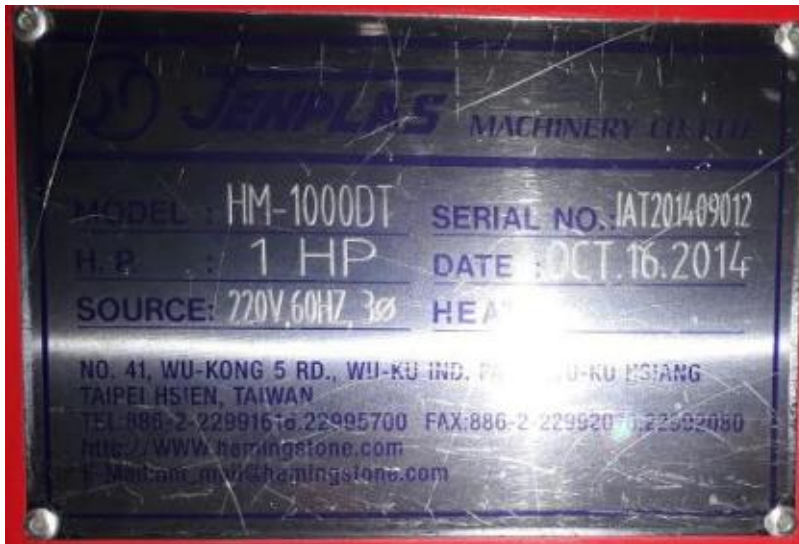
Máquina Impresora de estampados. Fuente: Empresa Plasmar s.a
